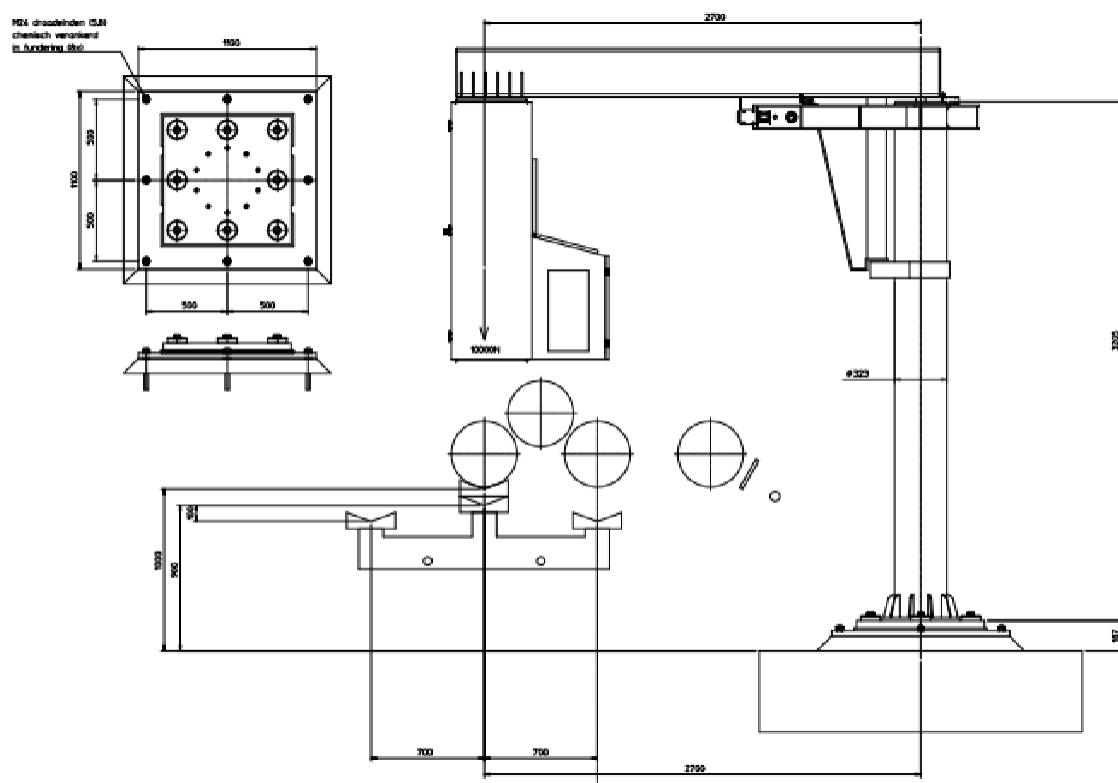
Estrutura mecânica com gabinete com sonda de teste e dispositivo com lixa rotativa
